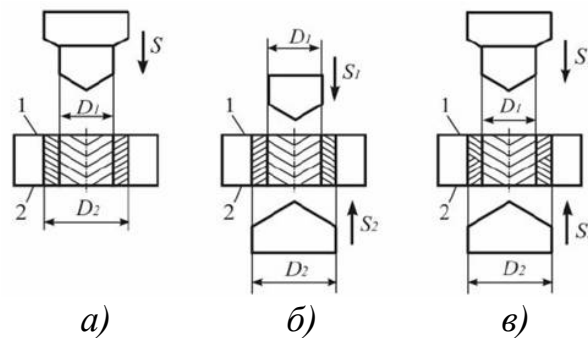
Схема обробки отворів: 1 – вхідна поверхня заготовки; 2 – вихідна поверхня заготовки; а) – схема оброблення отвору ступінчастим інструментом при постійній подачі; б) – схема оброблення отвору зі змінною напрямком подачі; в) – схема оброблення отвору ступінчастим інструментом зі змінною напрямку подачі [2].
